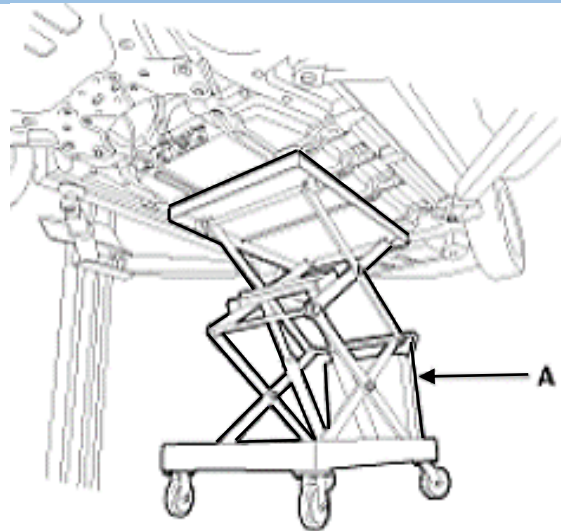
Mesa de elevación para desmontaje de batería. Fuente: Kia.
